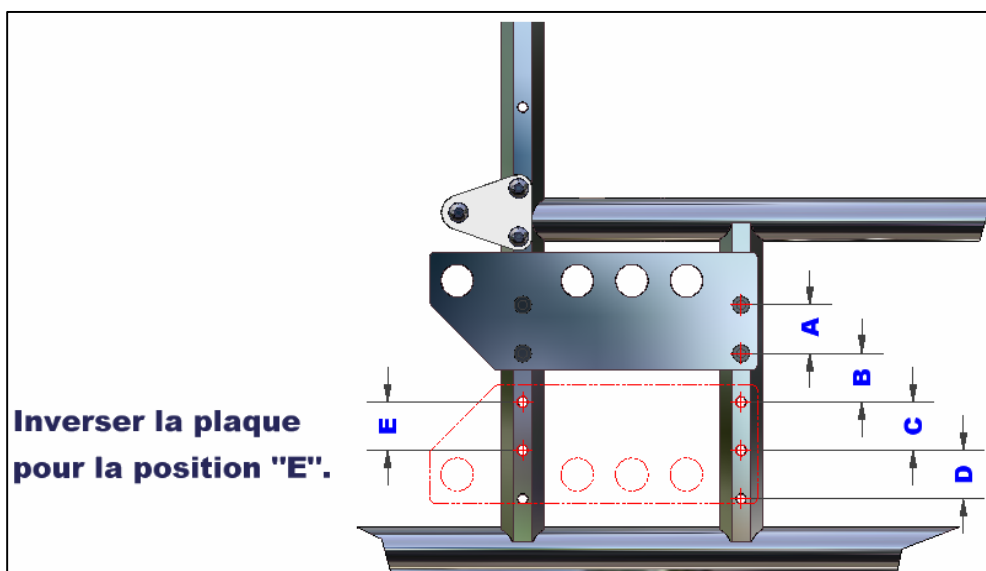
A : Hauteurs (positions) d'ajustement de la plaque multiposition.
